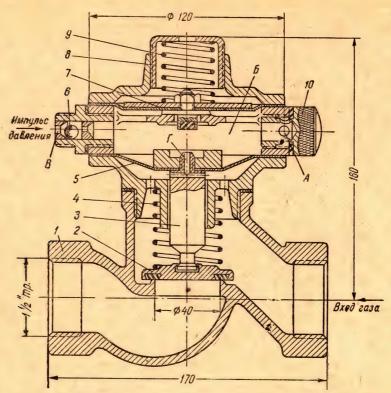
Предохранительный запорный клапан типа ПКК-40.
